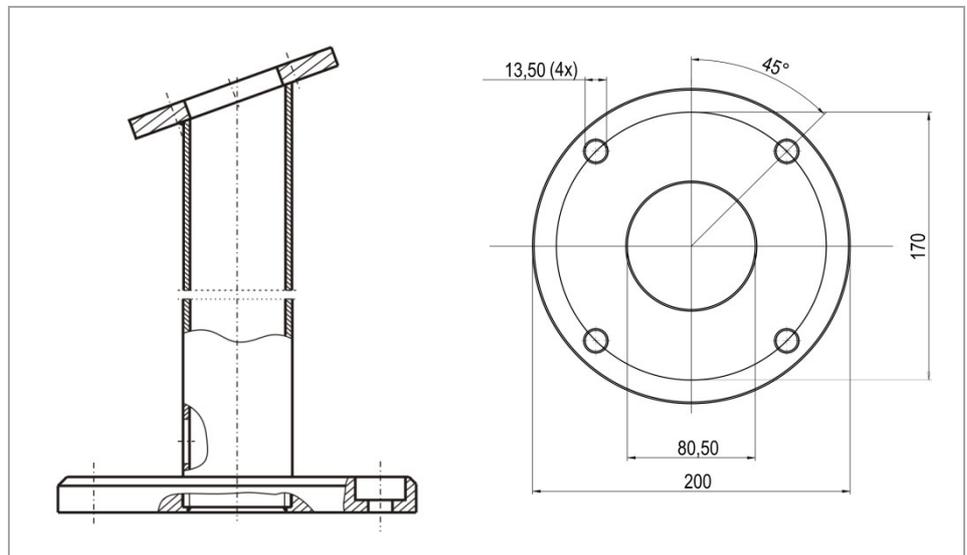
Standfuß - Bohrbild Bodenplatte
